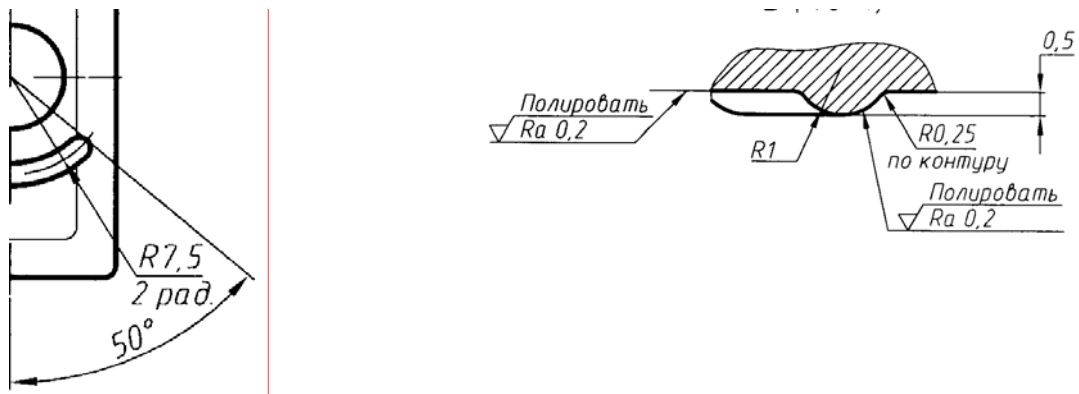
Фрагмент чертежа обжимки для выштамповки сегментных лунок
